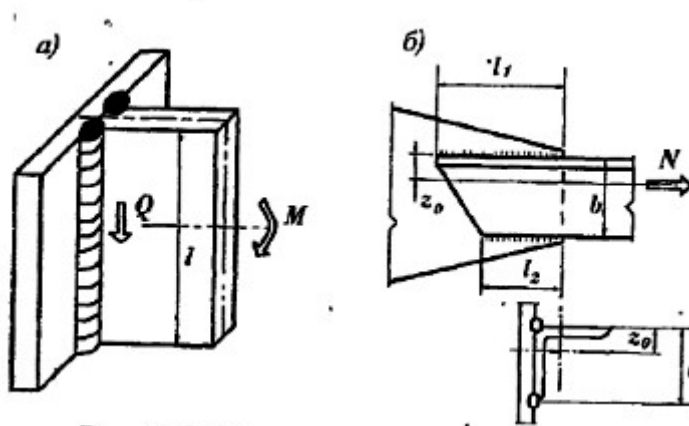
К расчету сварных соединений с угловыми швами: а) – на момент и поперечную силу; б) – приварка уголка.
